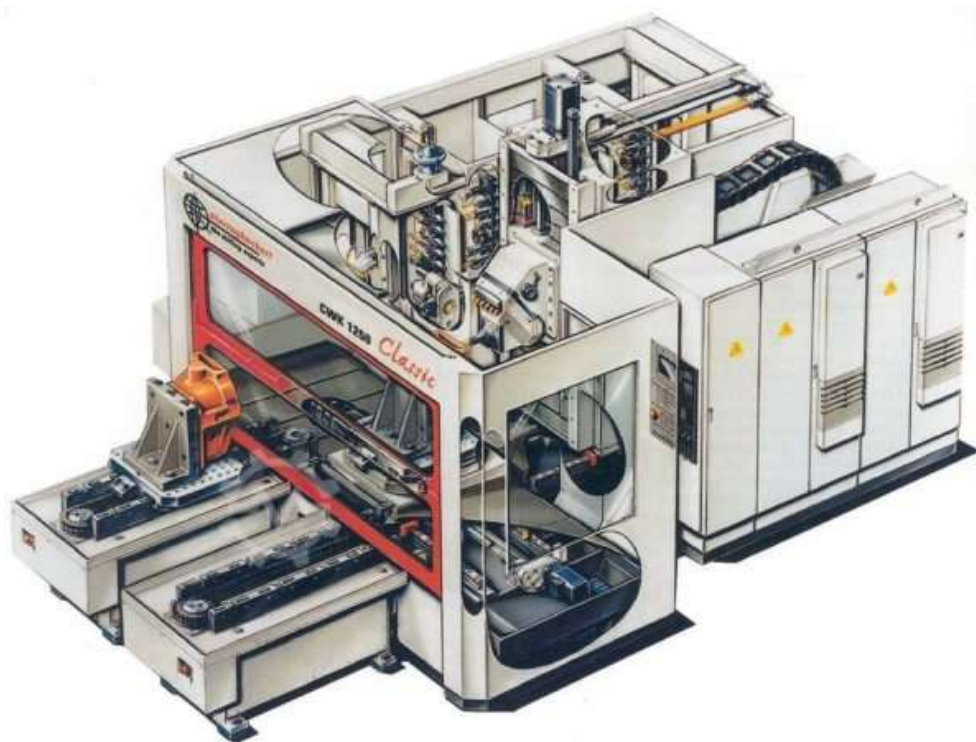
Горизонтальный фрезерный обрабатывающий центр Hecker CWK 1250
